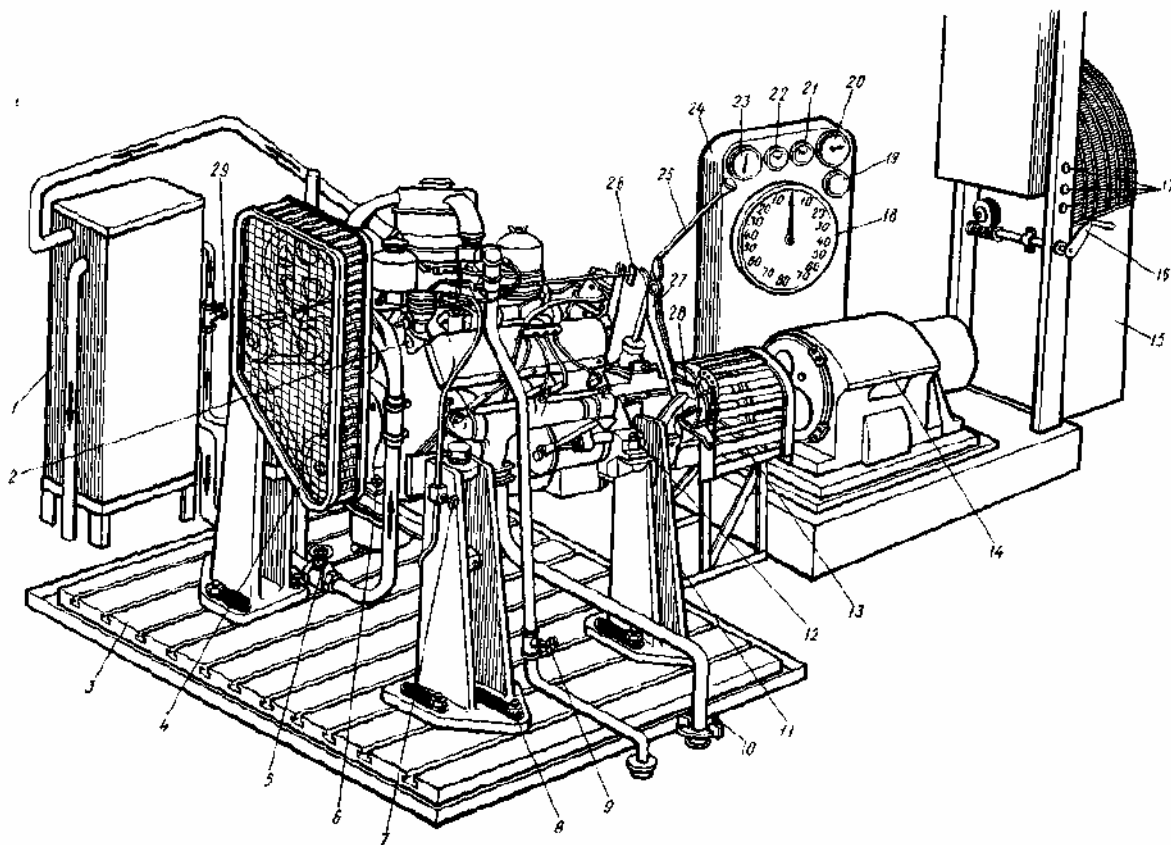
Стенд для обкатки и испытания двигателей: 1 – бак; 2 – двигатель; 3 – плита; 4 и 13 – решетки; 5, 9 и 29 – вентили; 6, 8 и 12 – элементы крепления двигателя; 7 – кран; 10 – элементы крепления газоотводной трубы; 11 – стойка; 14 – электромашина; 15 – реостат; 16 – рукоятка управления реостатом; 17 – кнопки; 18 – шкала; 19 – сигнализатор; 20 – тахометр; 21 и 22 – термометры; 23 – манометр; 24 – корпус; 25 – рычаг коробки передач; 26 – тяга; 27 – рычаг ручного тормоза; 28 – педаль
